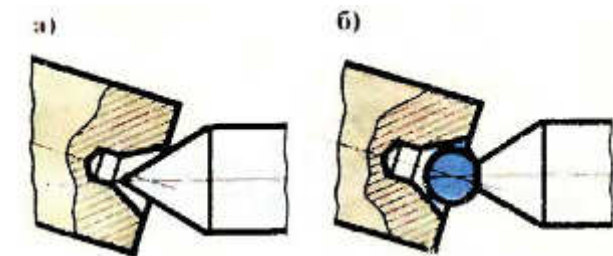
Схема наладки токарного станка для обработки конической поверхности (конуса) способом смещения задней бабки
